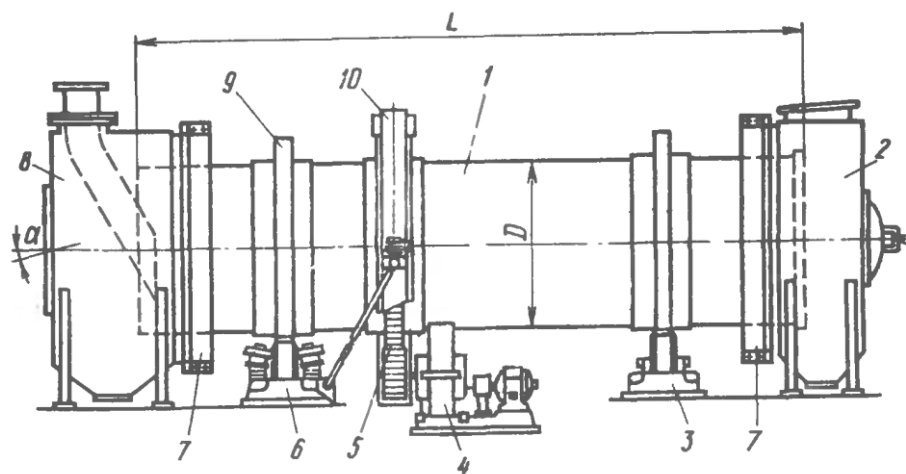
Схема і загальний вид барабанної сушарки
